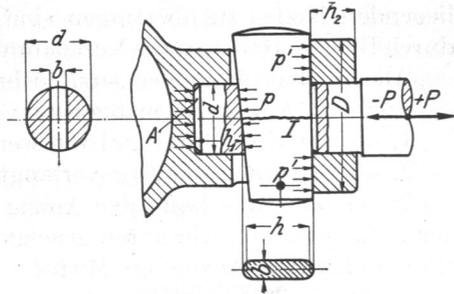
Befestigung einer Kolbenstange in einem Kreuzkopfe.
